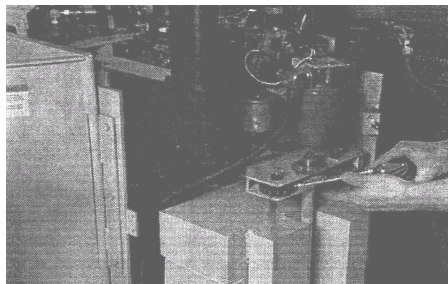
ENGRANAJES DE DIRECCIÓN
